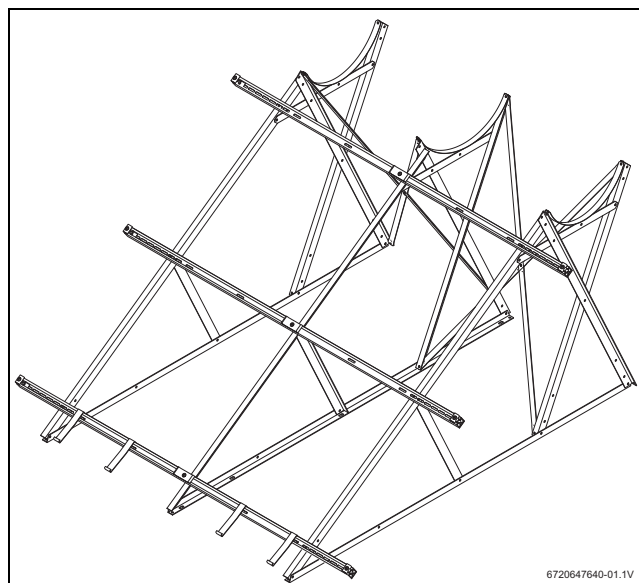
Vista de conjunto del soporte para cubierta plana (sistema de 300 l)
